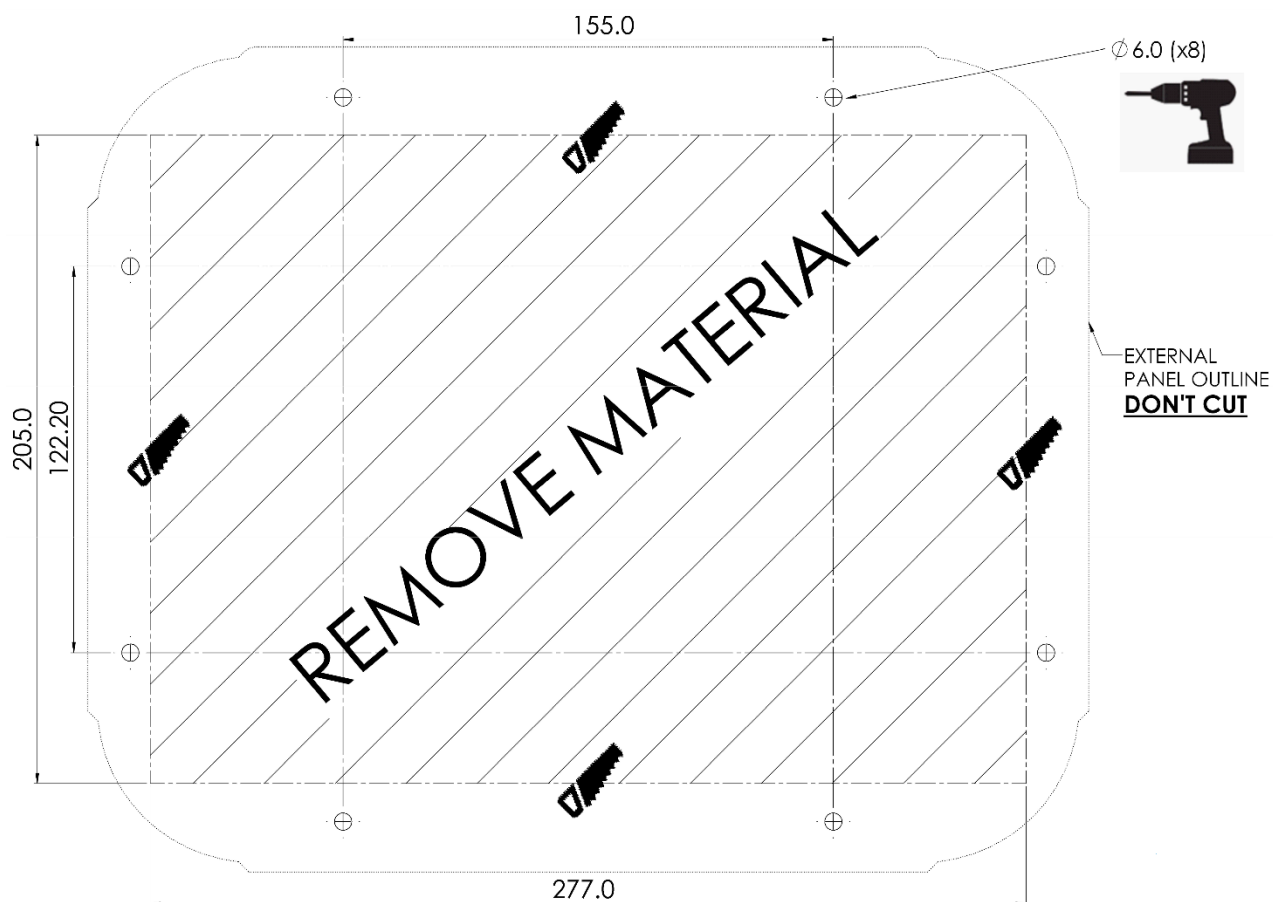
Dimensões de corte e perfuração do painel (milímetros)
